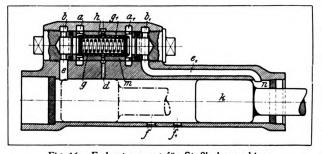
Federsteuerung für Stoßbohrmaschine.
